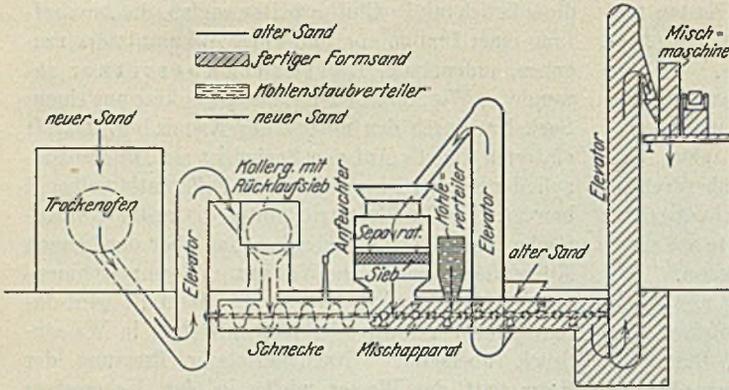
Schema einer Aufbereitungsanlage, Bauart Gutmann.
